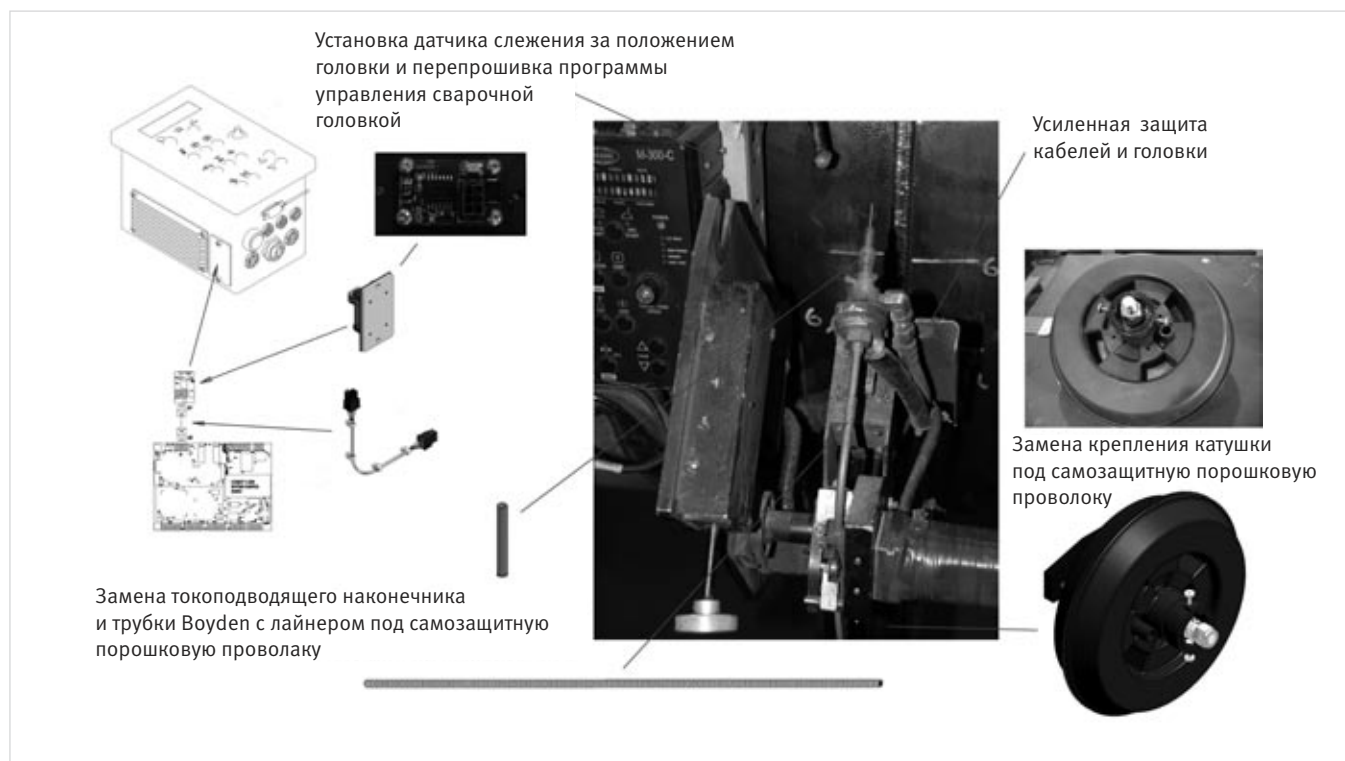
Узлы сварочной головки М300-С, подвергшиеся модернизации
